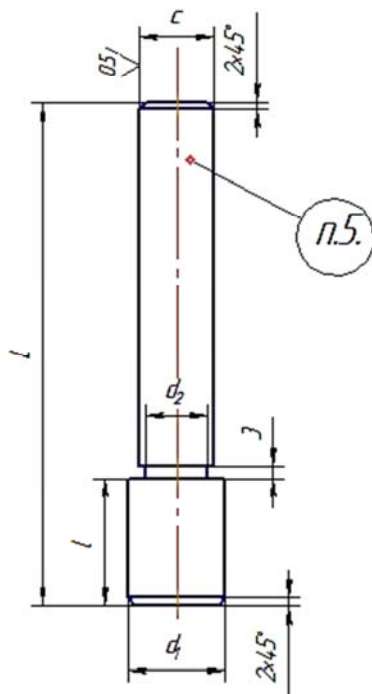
Конструкция колонки для створчатых металлических форм
